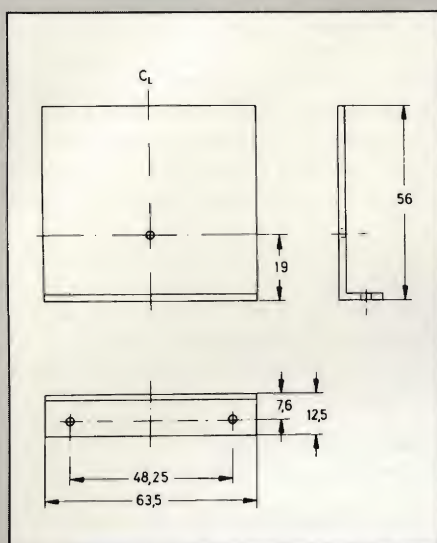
Dimensioni del radiatore di calore sul quale deve essere montato il transistor dello stadio finale di riga BU 806; dimensioni indicate in mm, diametro fori = 3,5 mm.
